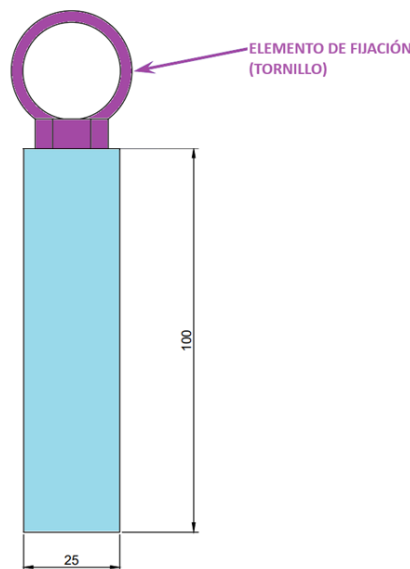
Esquema de montaje de la probeta mal templada, P805-fallo.
